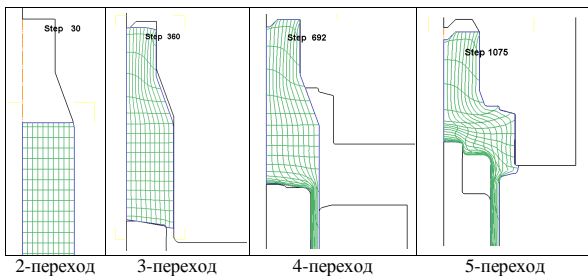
Конфигурация формообразующего инструмента и обрабатываемой заготовки по предлагаемой технологии на момент начала перехода ХОШ
